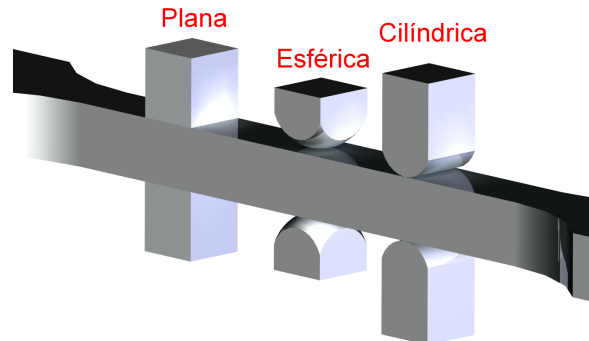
Tipos de sapatas para contato com corpo de prova plano.
